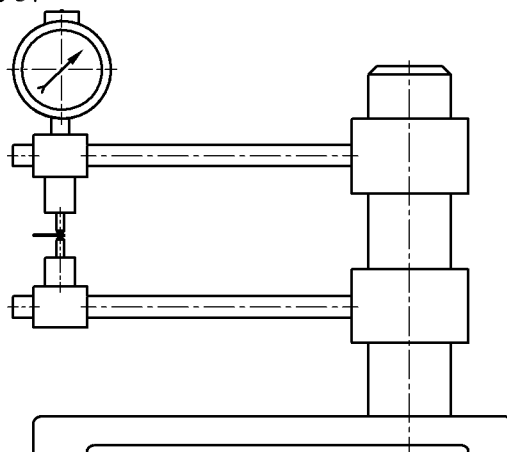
Приспособление для замера глубины выдавливаемой канавки
